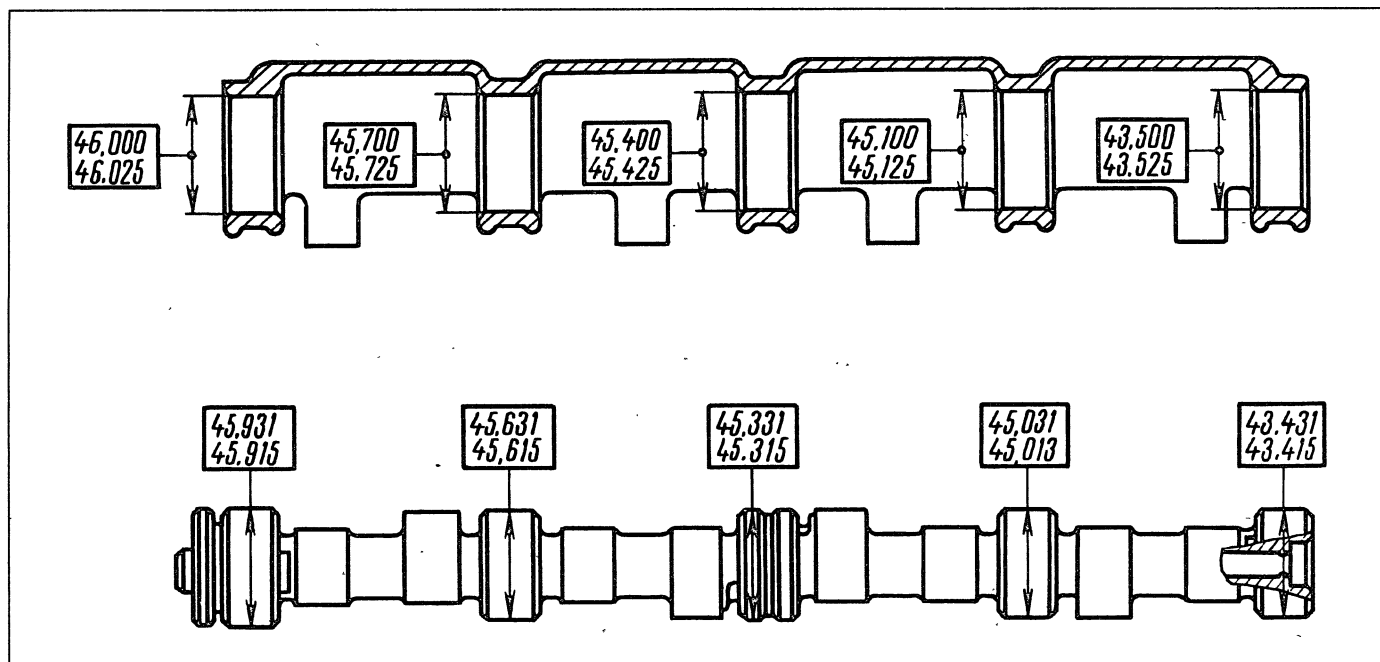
Основные размеры распределительного вала и корпуса подшипников
